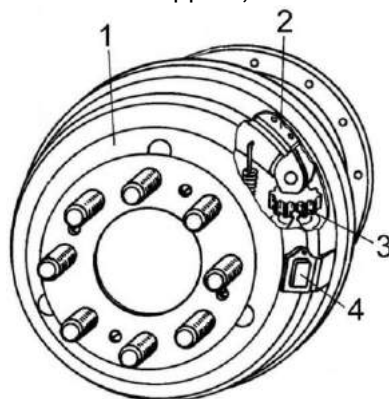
Регулировка механизма управления скоростью движения
